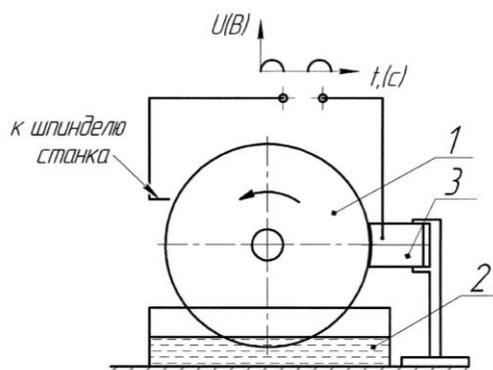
Схема установки для электрохимической правки алмазных кругов на металлической связке. Алмазный круг устанавливают непосредственно на шпиндель станка. Чтобы уменьшить разбрызгивание электролита привод главного движения станка был модернизирован. Двигатель был подключен через преобразователь частоты питающего тока. Это позволило снизить частоту вращения при правке до  $144 \text{ мин}^{-1}$ . В сочетании с системой защитных кожухов это позволило практически исключить выброс электролита из зоны правки.
